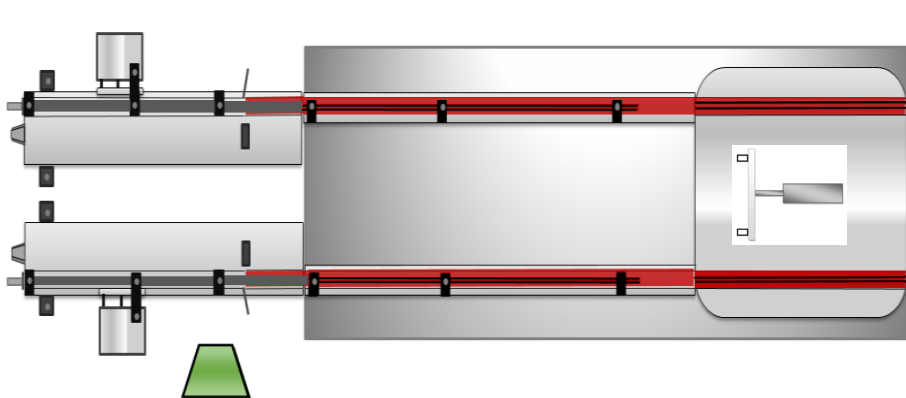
Vista de la planta, posición intermedia con prodcuto
